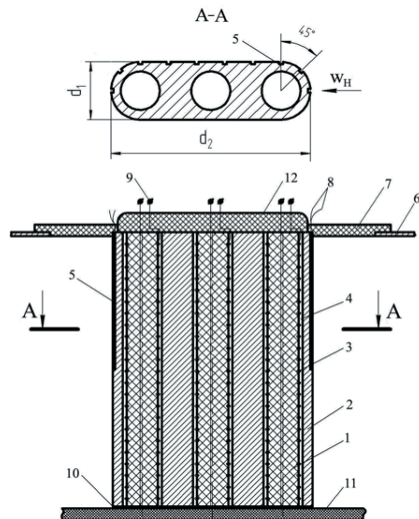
Труба-калориметр: 1 – стержень нагревателя; 2 – плоско-овальная труба; 3 – нагреватель; 4 – корундовая засыпка; 5 – канавки для термопар; 6 – верхняя трубная доска; 7 – крышка калориметра; 8 – провода термопар; 9 – разъем нагревателя; 10 – теплоизолирующая прокладка; 11 – нижняя трубная доска; 12 – теплоизолирующая крышка
